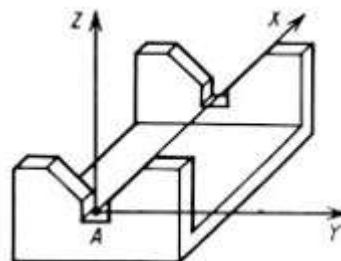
Призми для встановлення заготовок великої довжини
